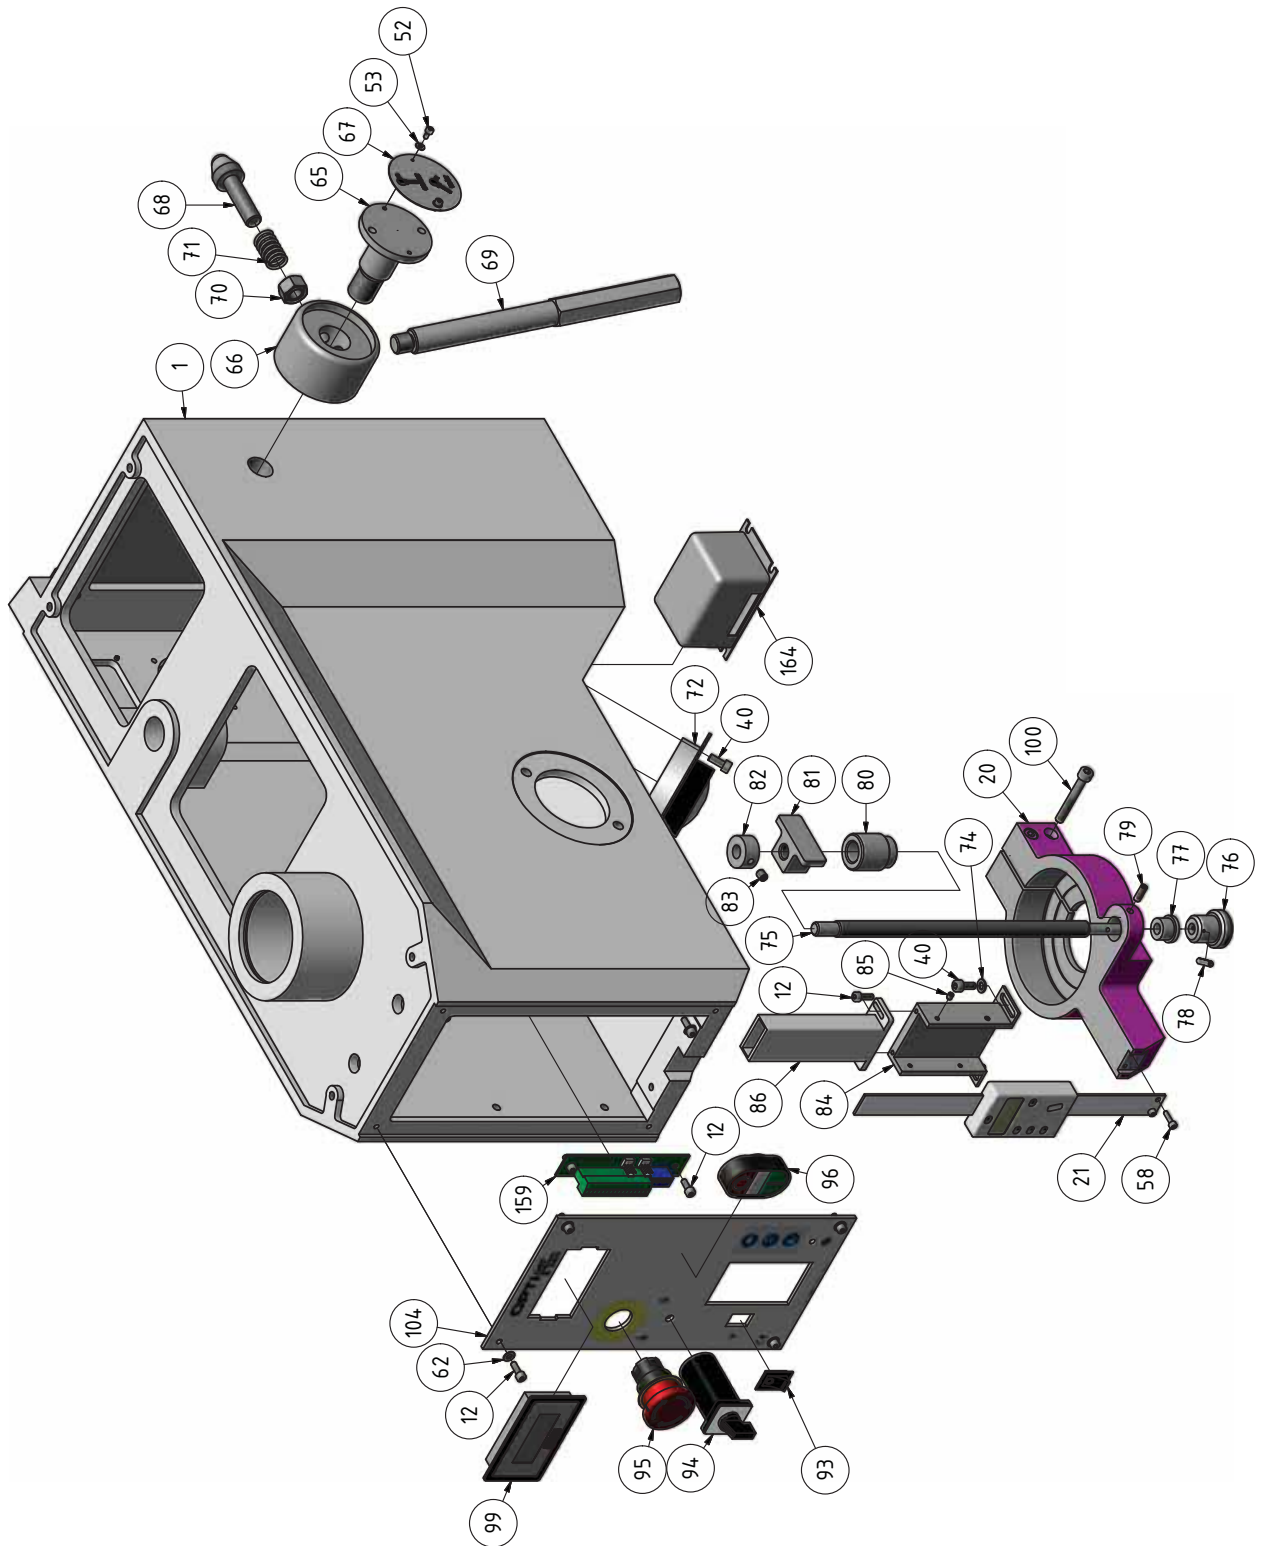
Bohrkopf 4 von 5 - Drilling head 4 of 5
